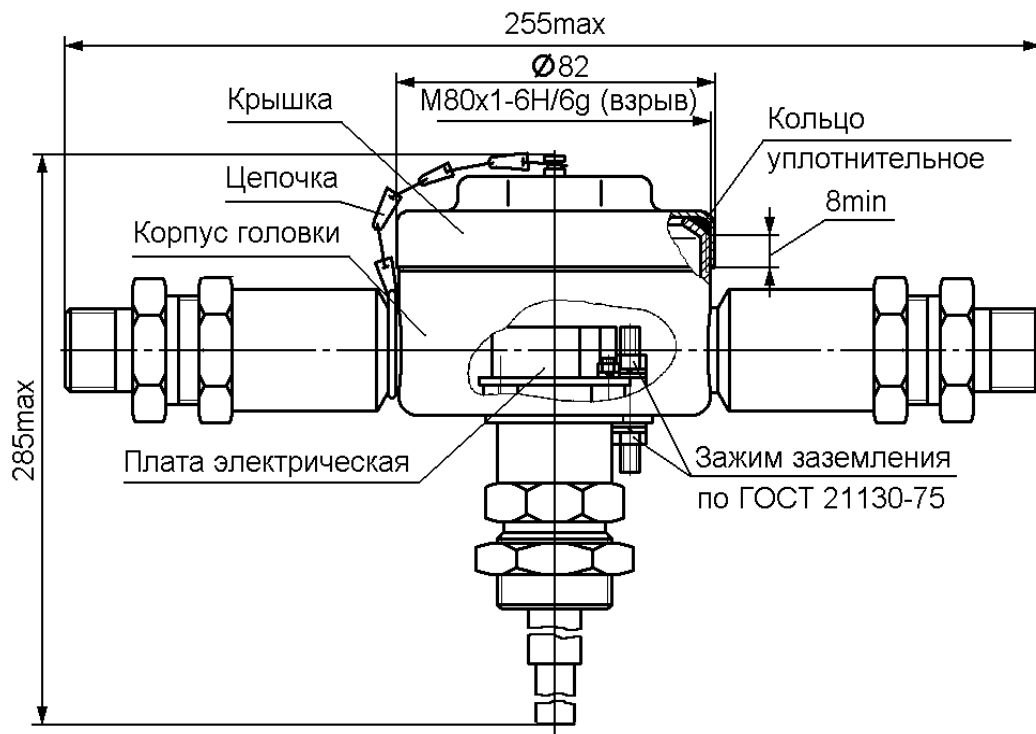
Габаритный чертёж ИП103-2В/П-Н в корпусе из нержавеющей стали (остальное – на рис. А.1)
